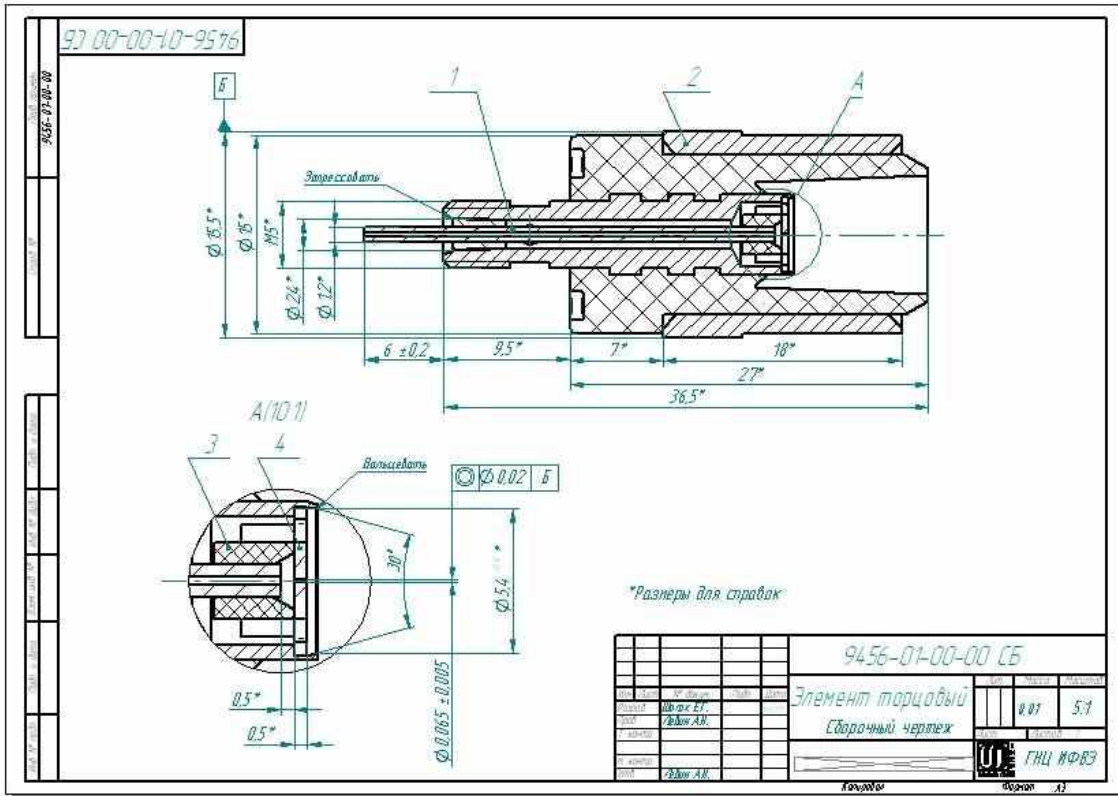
Сборочный чертёж торцевого элемента ДТМ
